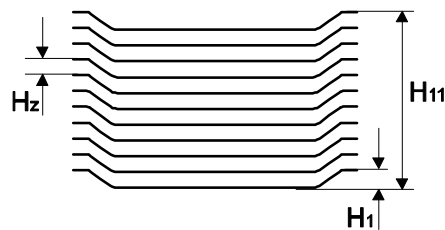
Altezza della pila intermedia H_z con 11 pezzi di stoviglie
